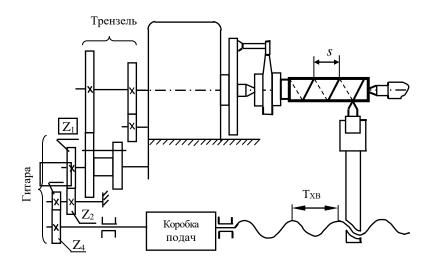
Схема нарезания резьбы на токарновинторезном станке
